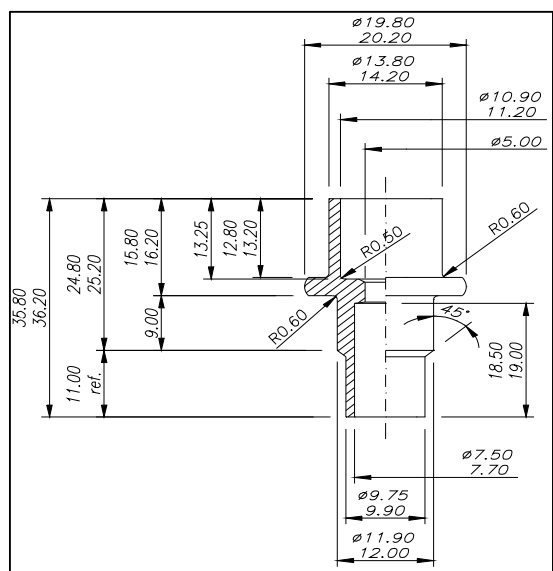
Dimensões em mm dos terminais obtidos após operação de usinagem.
